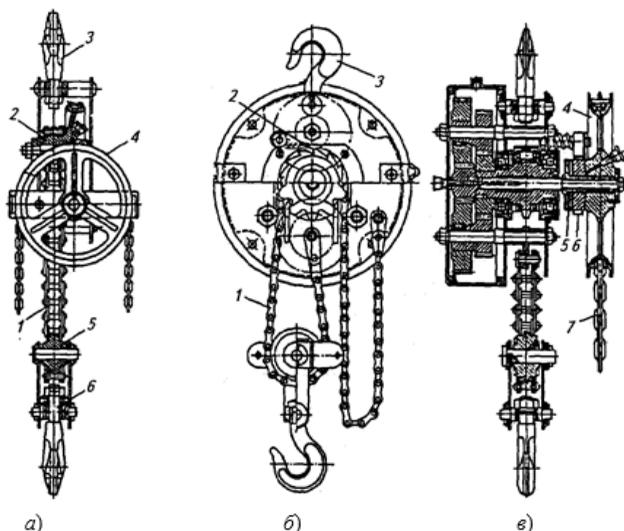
Ручные тали: а – червячная; б, в – шестеренная; 1 – пластинчатая цепь; 2, 5 – звездочки; 3 – крюк; 4 – приводное колесо; 6 – храповое колесо; 7 – цепь
